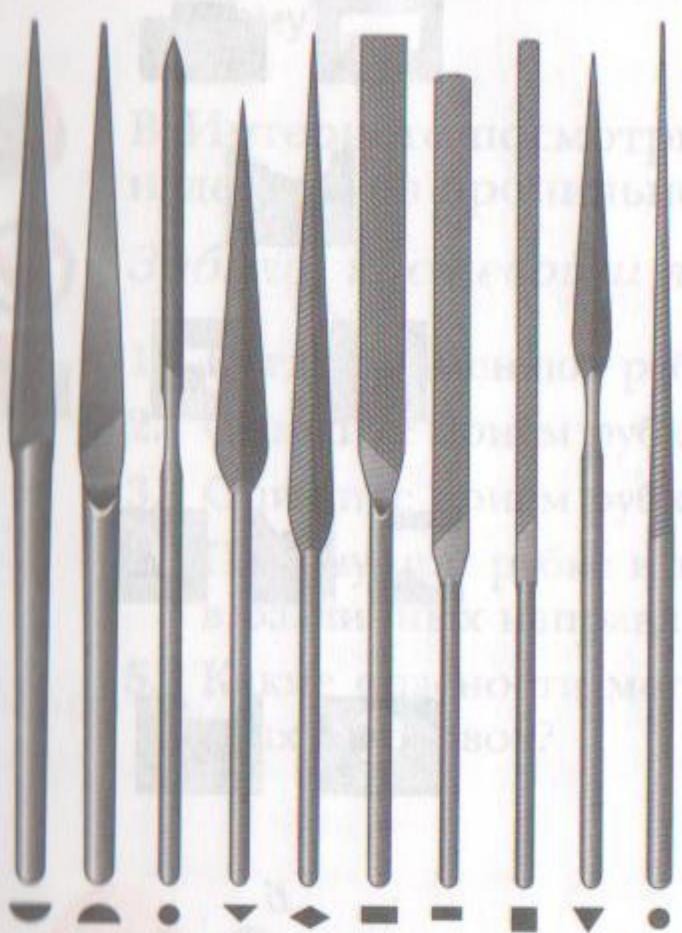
Надфили и их профили (фигуры поперечного сечения в рабочей части)
